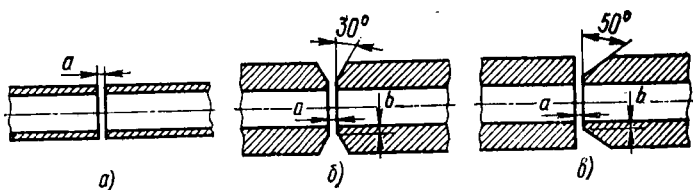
Формы стыков труб перед сваркой.
